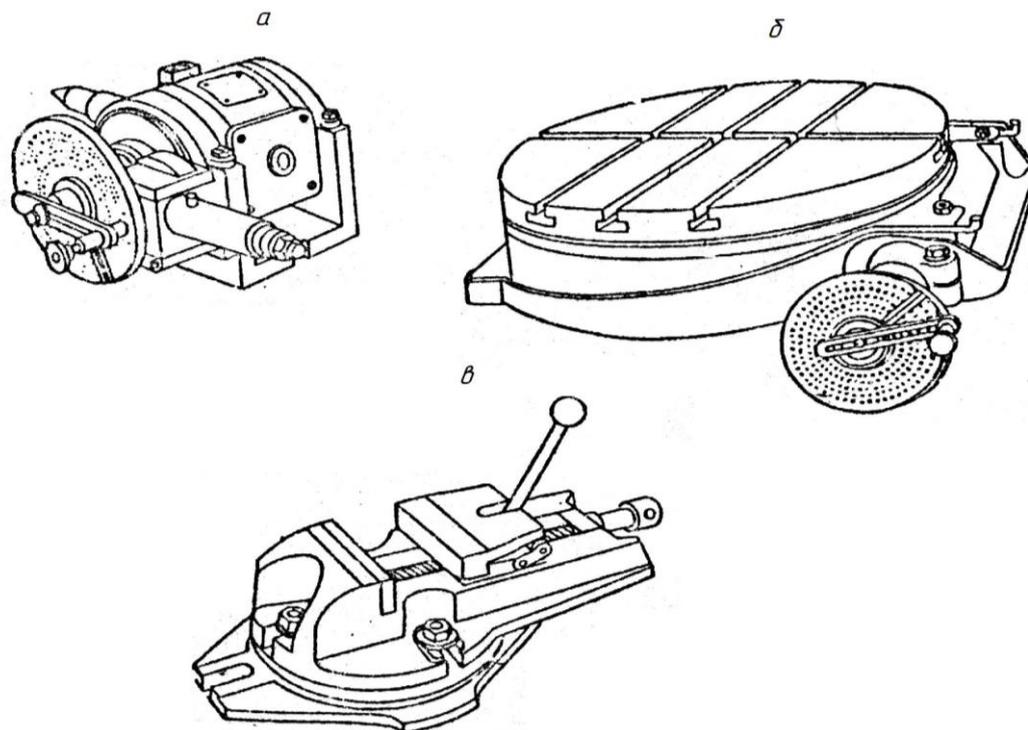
Приспособления к консольно-фрезерным станкам: а – делительная головка; б) – круглый стол; в) – машинные тиски
